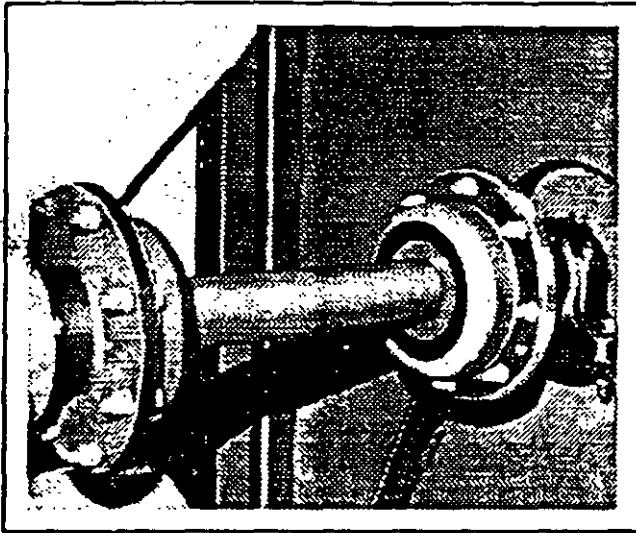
IMPULSOR DEL VENTILADOR DE EQUIPO, COPLÉ DE HULE NO LUBRICADO. E-27091-S
